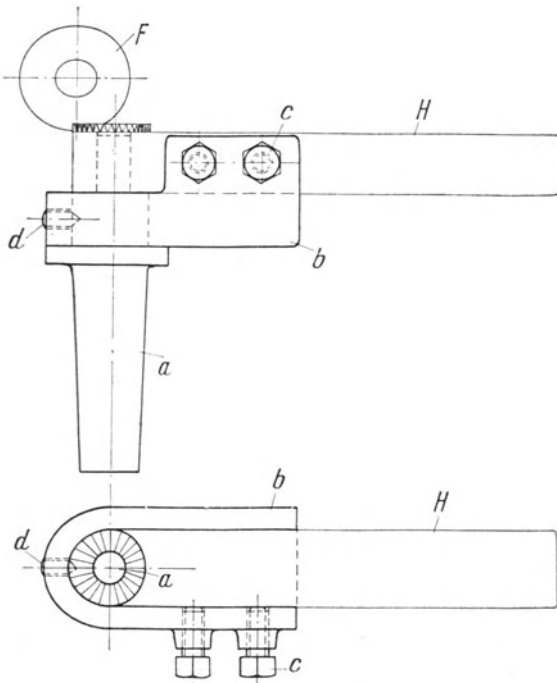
Fräsen des Zahnringes am Halter Abb. 516.
